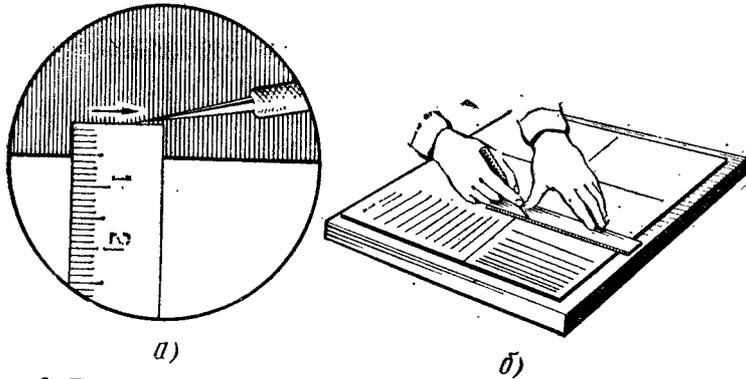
Прием откладывания размеров от кромки заготовки (а) и нанесения параллельных рисок (б)
